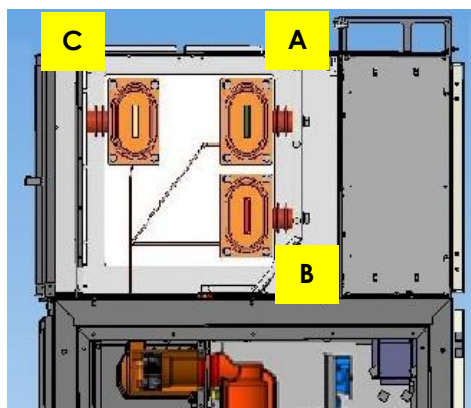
Соединения сборных шин КРУИТ «Спарта» при стыковке шкафов
